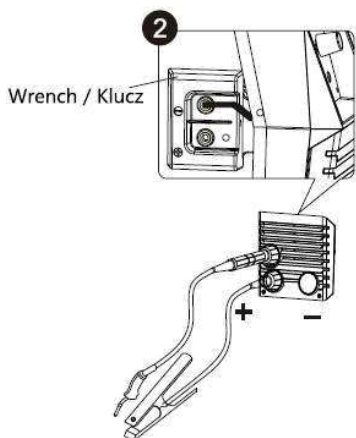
Příprava zařízení Fanmig pro svařování MIG / MAG.
